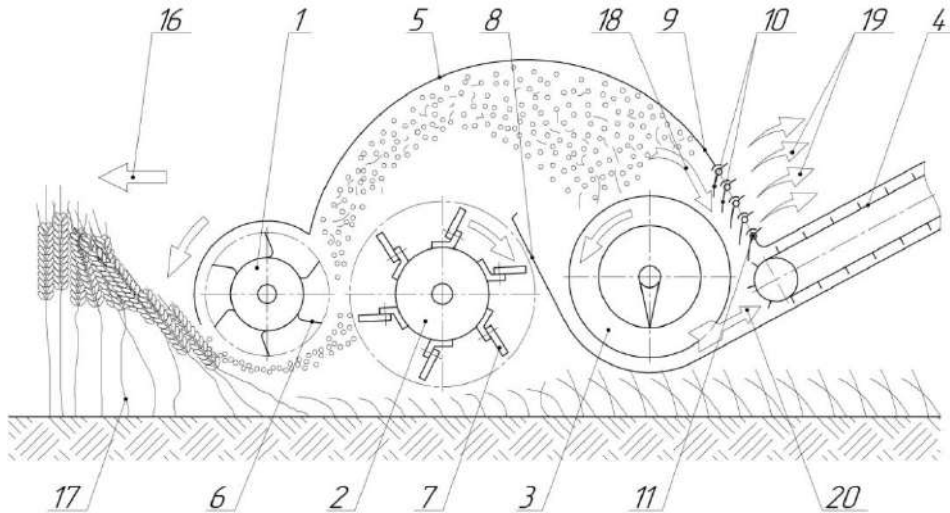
Принципиальная схема удаления полова из корпуса очесывающего адаптера (Пат № 2566017 РФ)
